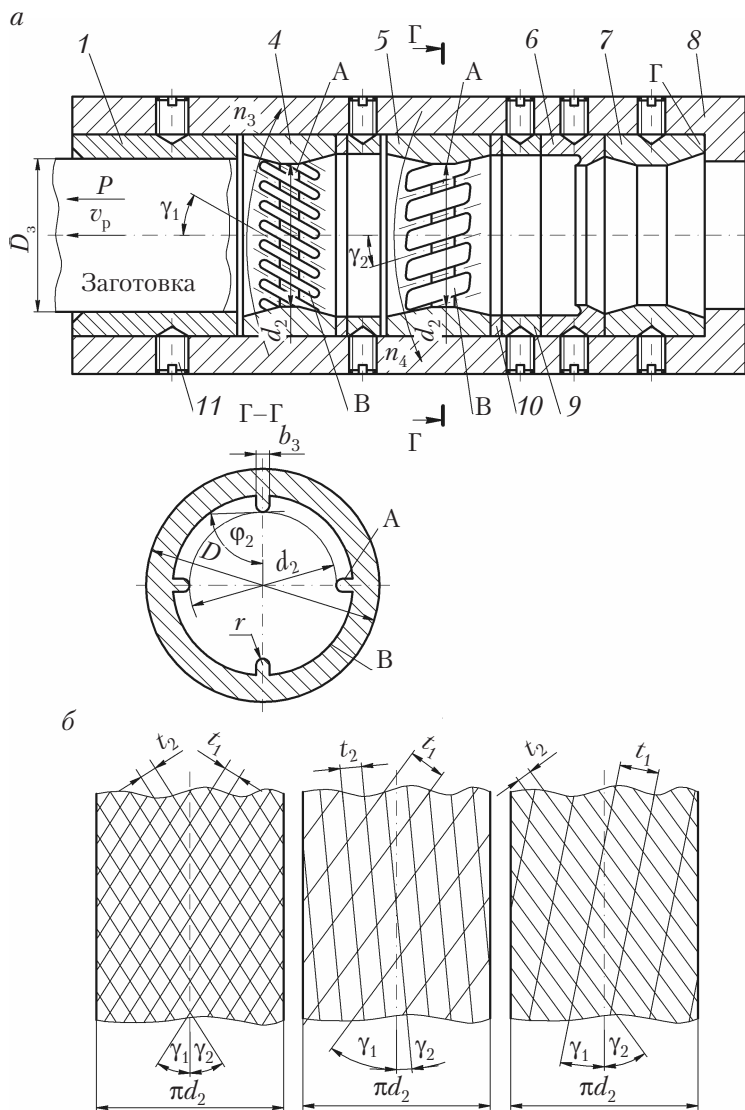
Комбинированный инструмент для обработки ППД резанием наружных цилиндрических поверхностей (а) и разновидности ЧЗРМР на развертках цилиндров (б)
